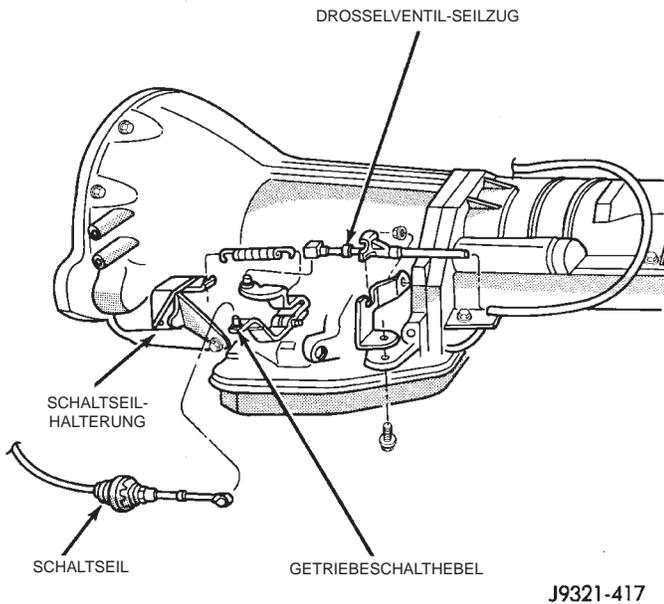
Schaltseilbefestigung am Getriebe-Typisch
